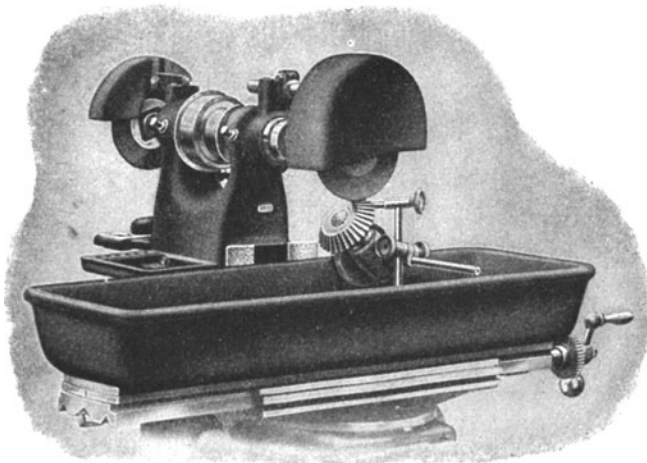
Werkzeugschleifmaschine (Ausführung der Wanderer-Werke A.-G., Chemnitz).
